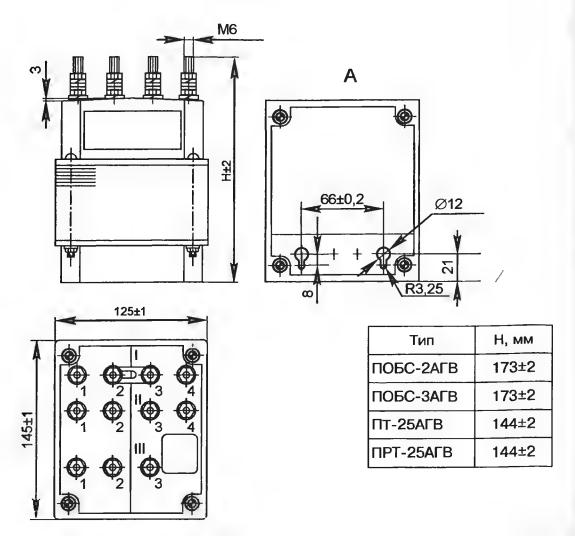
Установочные, присоединительные и габаритные размерытрансформаторов ПОБС-2AГВ, ПОБС-3AГВ, ПТ-25AГВ, ПРТ-25AГВ
